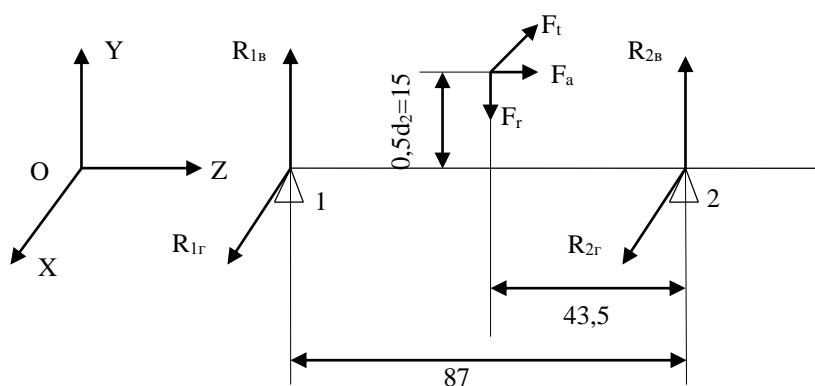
Реакции опор для подшипников быстроходного вала от радиальных сил
